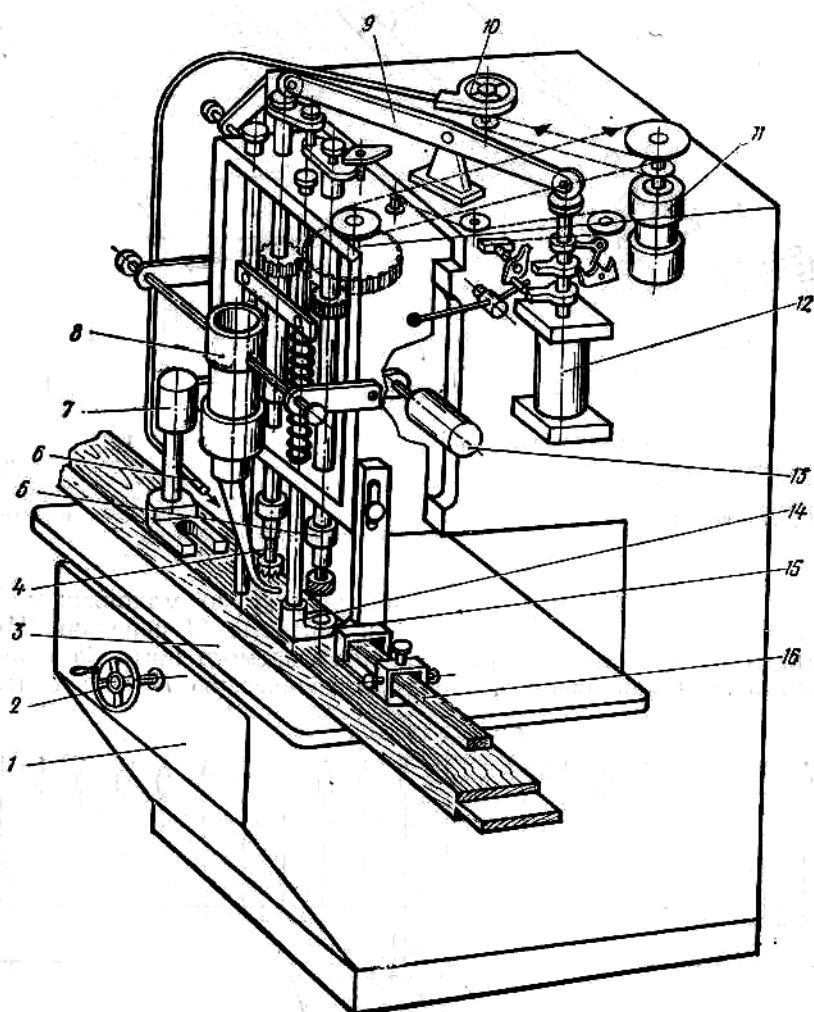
Станок для высверливания и заделки сучков СВСА-2:
